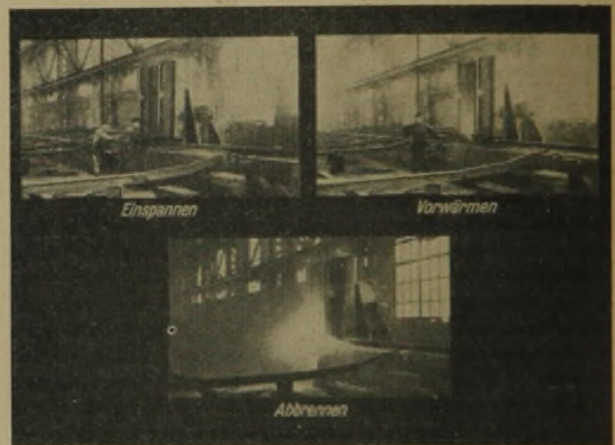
Widerstandsschweißung, Abrennschweißen von Eisenbahnschienen
